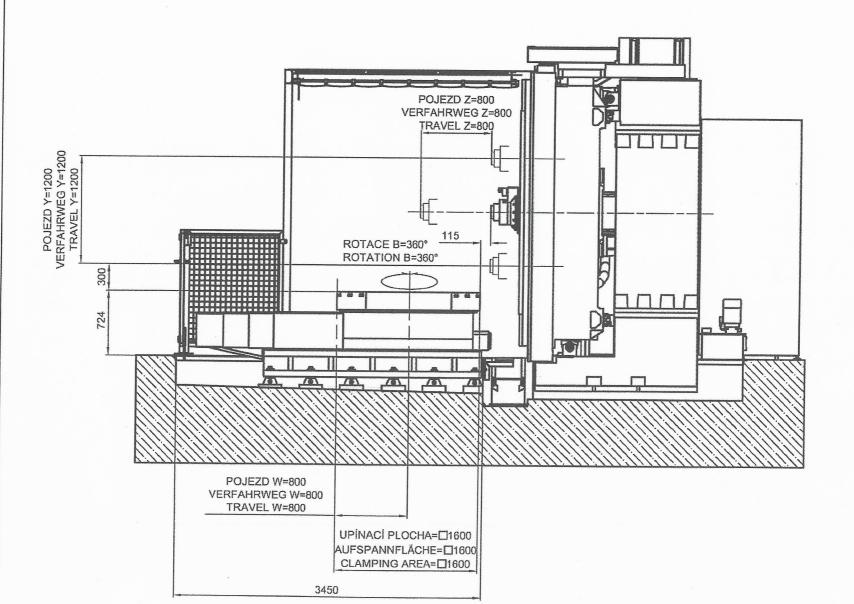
Bearbeitungsbereich der Maschine
